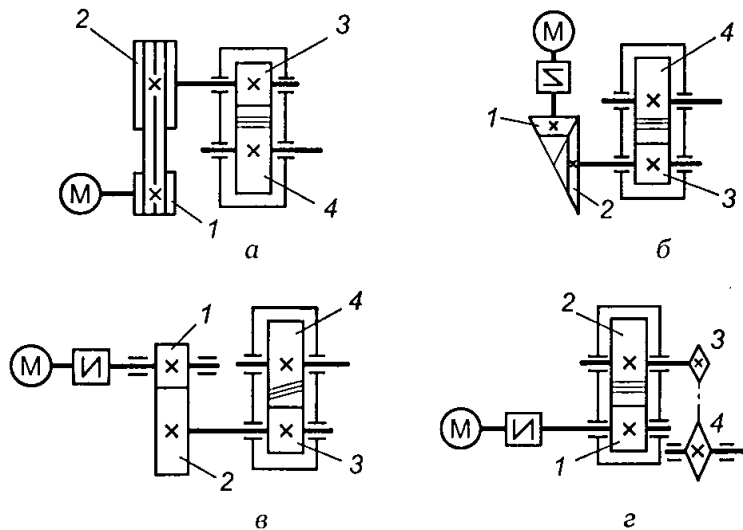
Схемы двухступенчатых приводов: *а* — ременная передача и цилиндрический редуктор; *б* — коническая передача и цилиндрический редуктор; *в* — двухступенчатая цилиндрическая передача; *г* — цилиндрический редуктор и цепная передача; 1, 3 — ведущие звенья; 2, 4 — ведомые звенья
